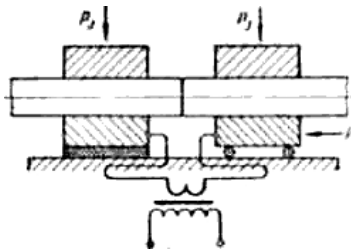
Схема процесса стыковой сварки: P_z — усилие зажатия; P_{oc} — усилие осадки
